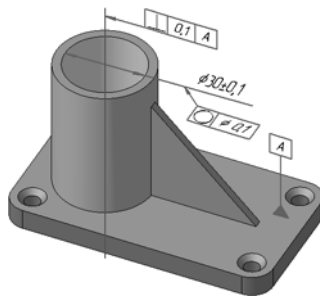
Пример простановки допуска формы и расположения поверхности
